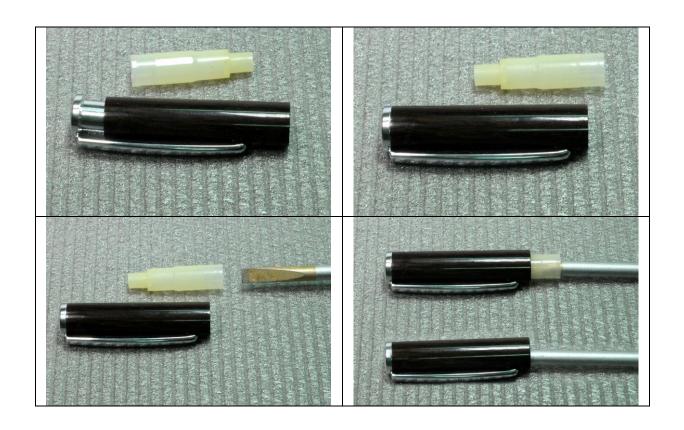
Prüfen ob Dichtung schon tief genug eingeschraubt wurde
